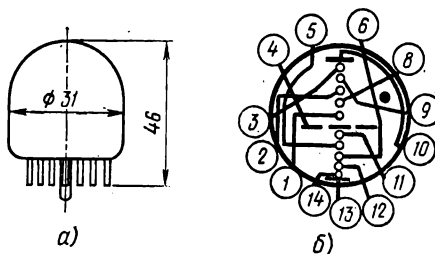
Габаритный чертеж (а) и цоколевка (б) индикаторной лампы ИН-4:
